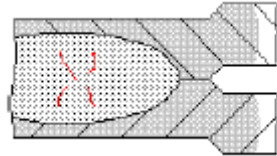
Representação de fissuras no ponto de soldadura
